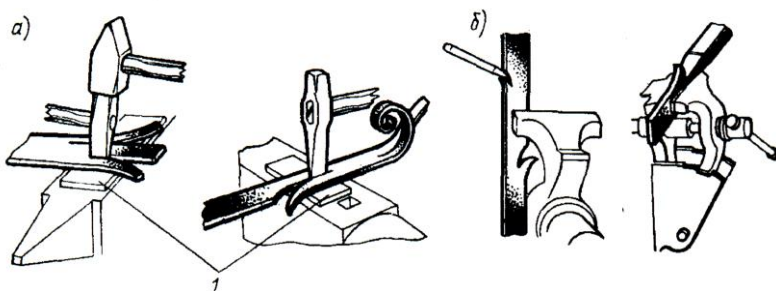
Способы разрубки и надрубки: а – на наковальне; б – в тисках; 1 – подкладка из мягкой стали или меди для предохранения зубила от затупления
